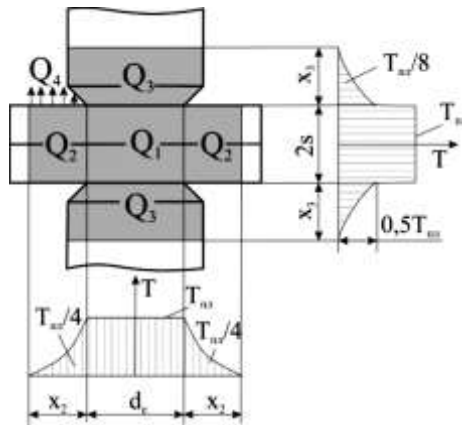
Розрахункова схема теплового балансу при точковому зварюванні
